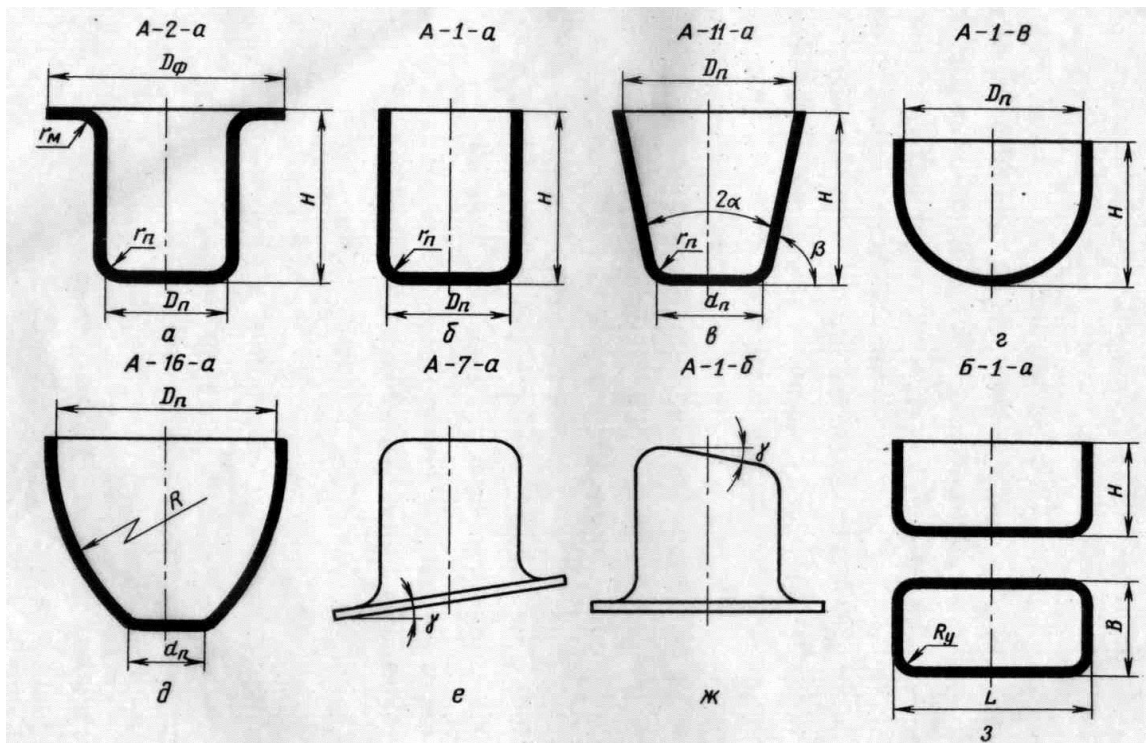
Типовые формы полых листовых деталей, изготавливаемых глубокой вытяжкой
